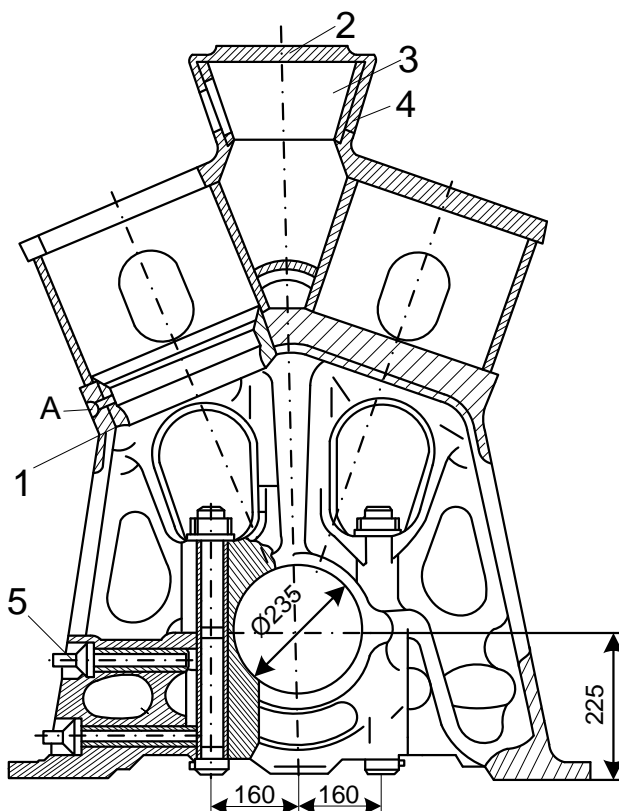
Блок дизеля Д49: 1 – кольцо опорного пояса; 2 - горизонтальная плита; 3 – ребро; 4 – боковой лист; 5 – горизонтальный болт
